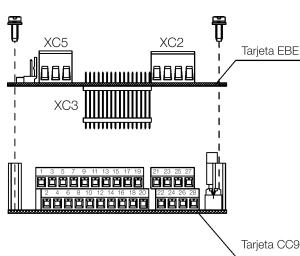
Encaje del conector XC3 EBE - Vista frontal
